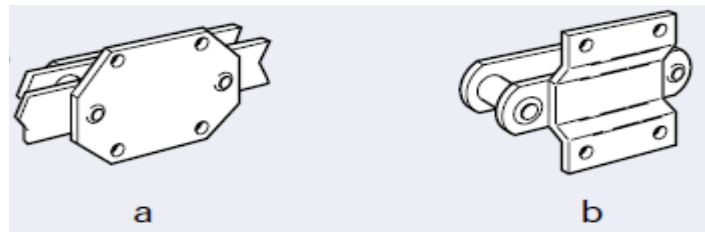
Accesorios tipo G. a) Accesorio tipo G de placa externa, b) Accesorio tipo G soldado o remachado a la placa de unión.
